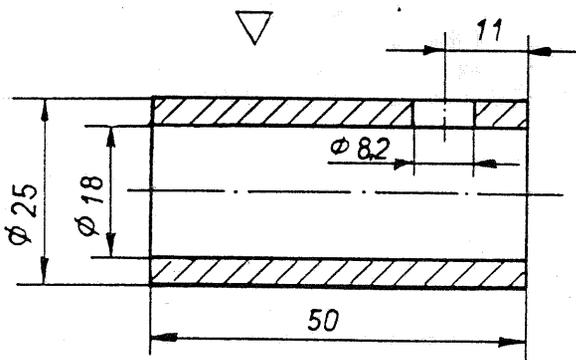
Tube destiné au réglage grossier de l'embrayage
